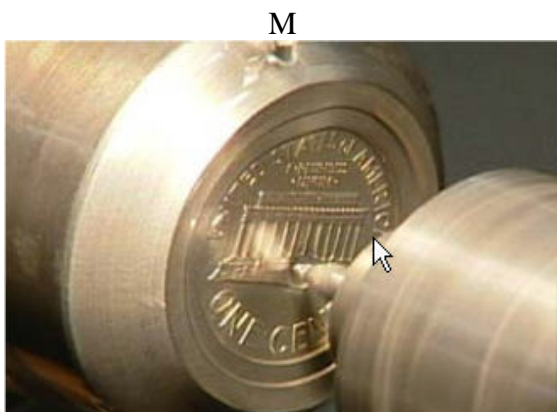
La herramienta de corte o fresa, tallando el punzón de máquina
